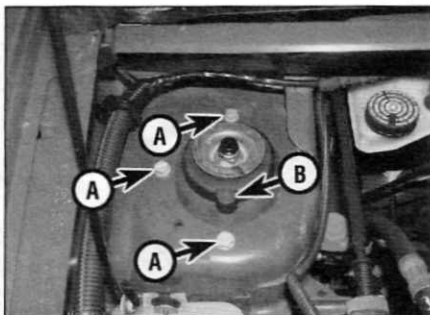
Болты (А) и установочный выступ (В) верхней опоры стойки подвески
